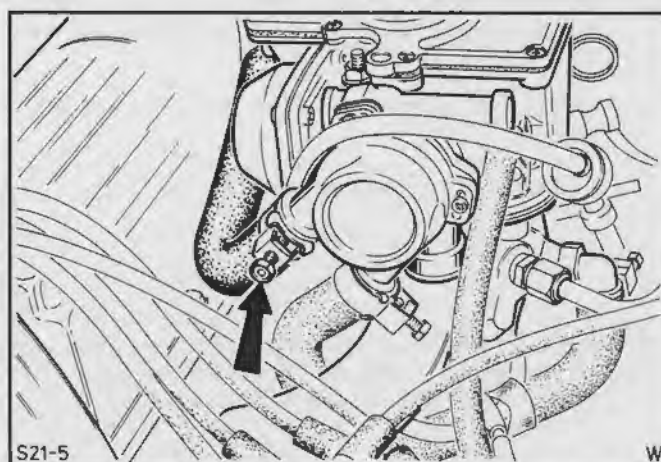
Monter varmeslangen på aut. choker (VV karburator vist)
